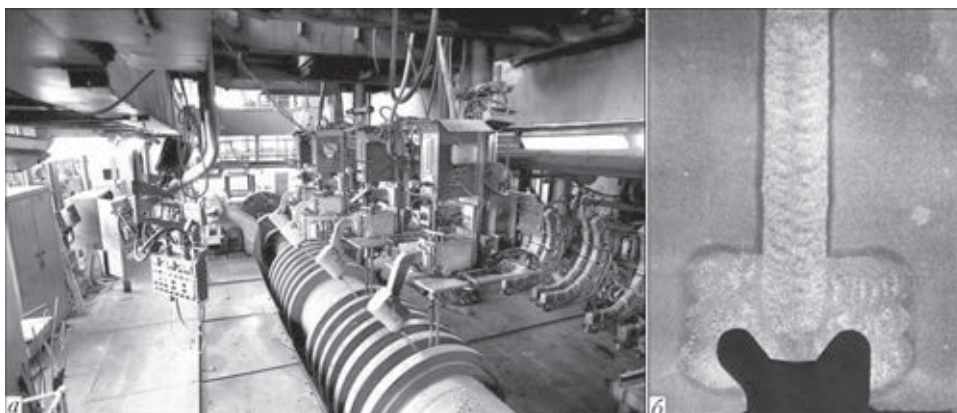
Автоматическая сварка под флюсом ротора паровой турбины мощностью 1000 МВт для АЭС (а) и макрошлиф металла сварного шва ротора паровой турбины (б)
